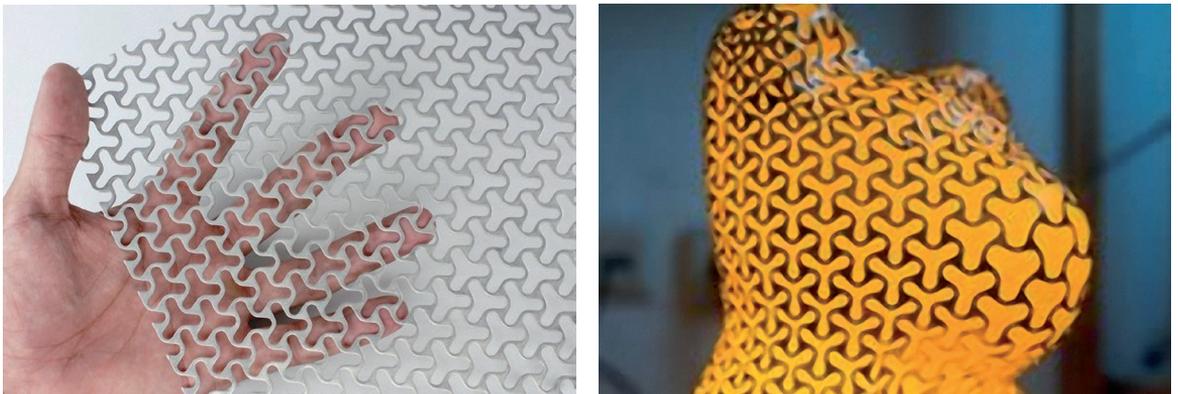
Drapierbares Lochblech, hier: Produkt Formetal® [Fotos: DINOSAURIER-Werkzeuge Trading GmbH]
